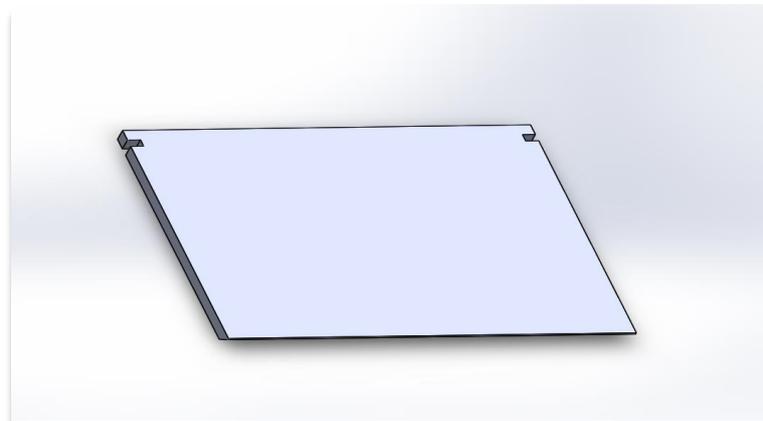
Ranura trasera para machihembrado de la pata izquierda.
